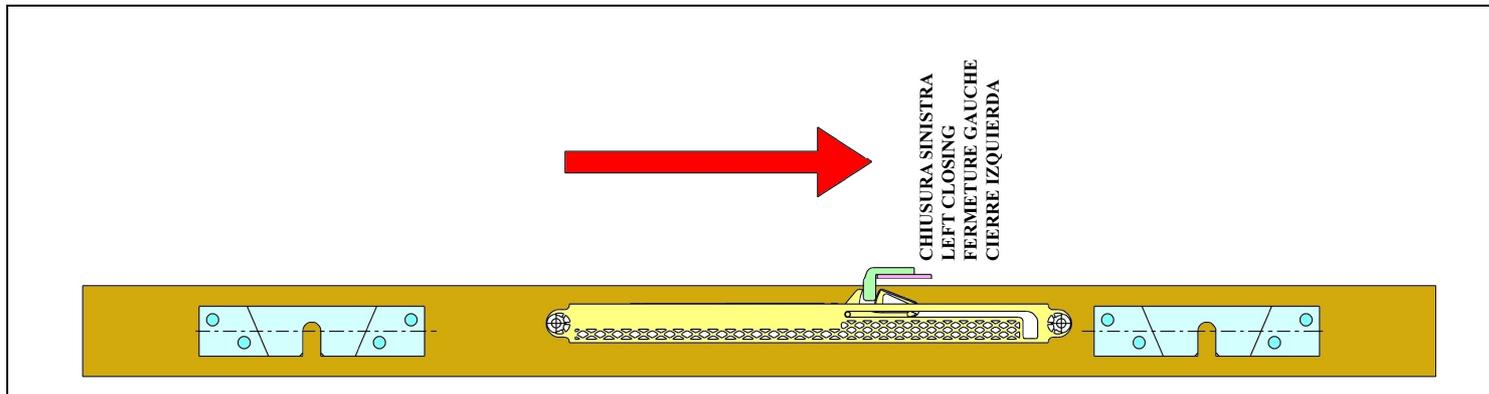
Montaggio dei particolari con chiusura a sinistra - Assembly instructions of the parts with left closing
